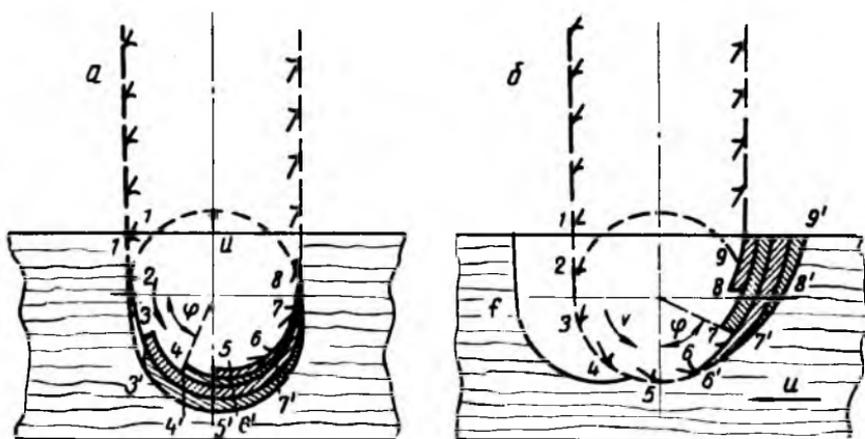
Схемы обработки гнезда фрезерными цепочками:
